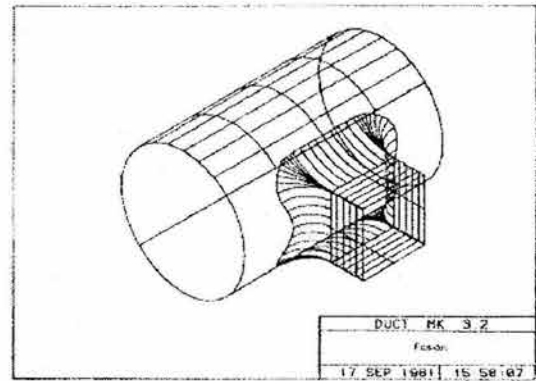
Superficie fundida (Delta Computer Aided Engineering)
